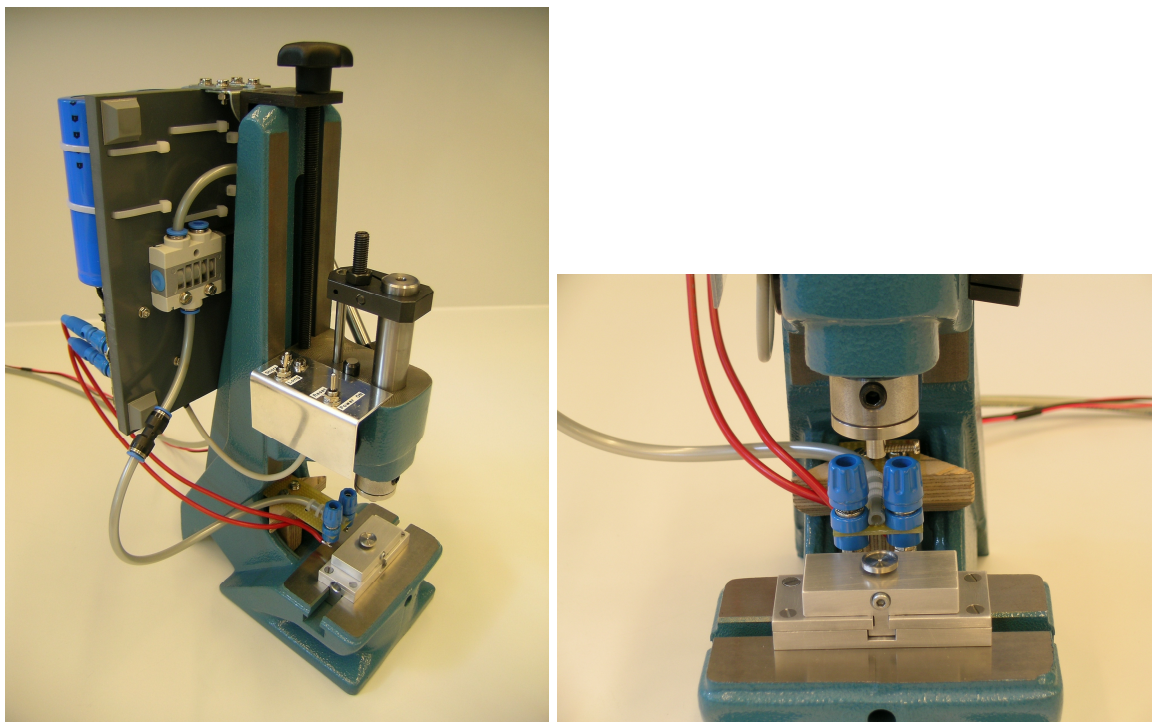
Zwei Ansichten des Geräts fürs Thermoschweißen.
